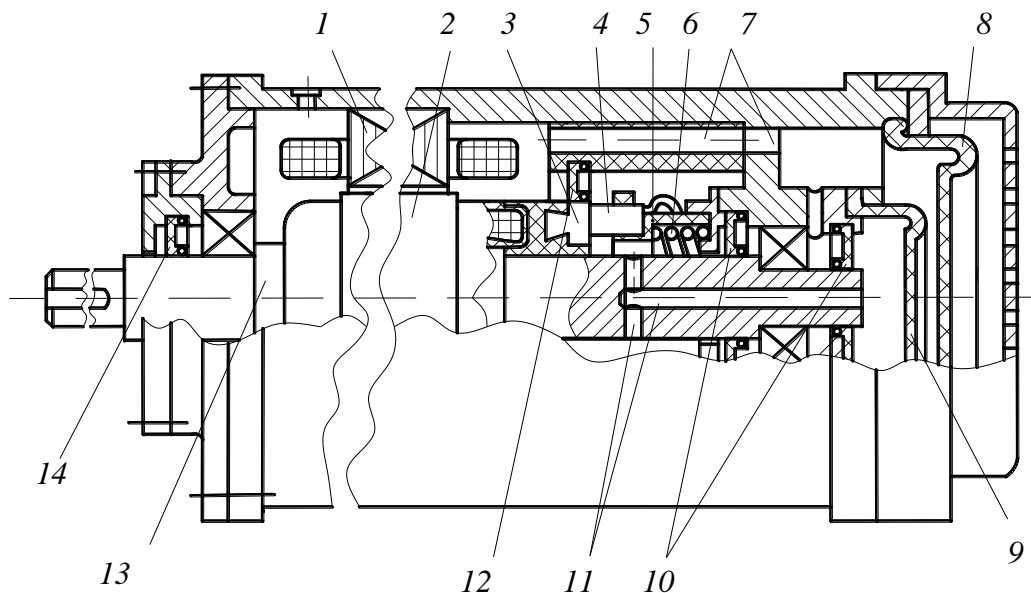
Конструктивная схема погружного коллекторного двигателя постоянного тока:
